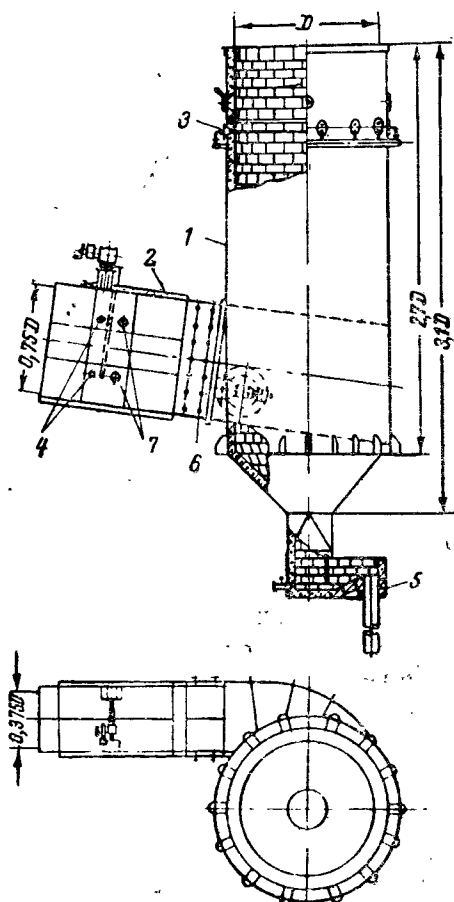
Мокрый прутковый золоуловитель МП-ВТИ. 1 — корпус; 2 — входной патрубок; 3 — оросительные сопла; 4 — смывные сопла; 5 — гидрозатвор; 6 — прутковая решетка; 7 — оросительные форсунки прутковой решетки
